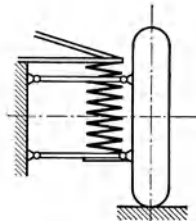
Schraubenfeder an Parallelogrammhebeln.
